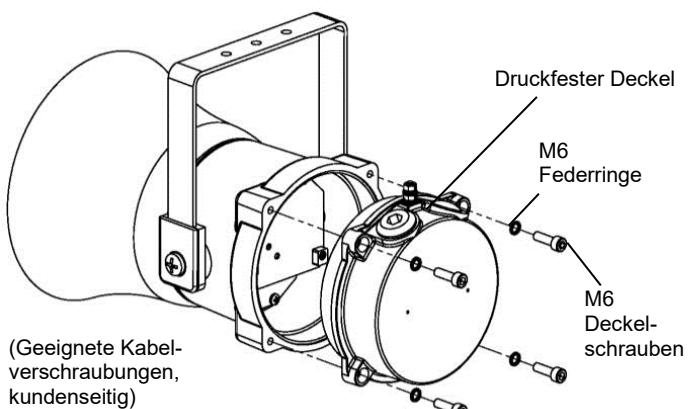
Zugang zum explosionsgeschützten Gehäuse
